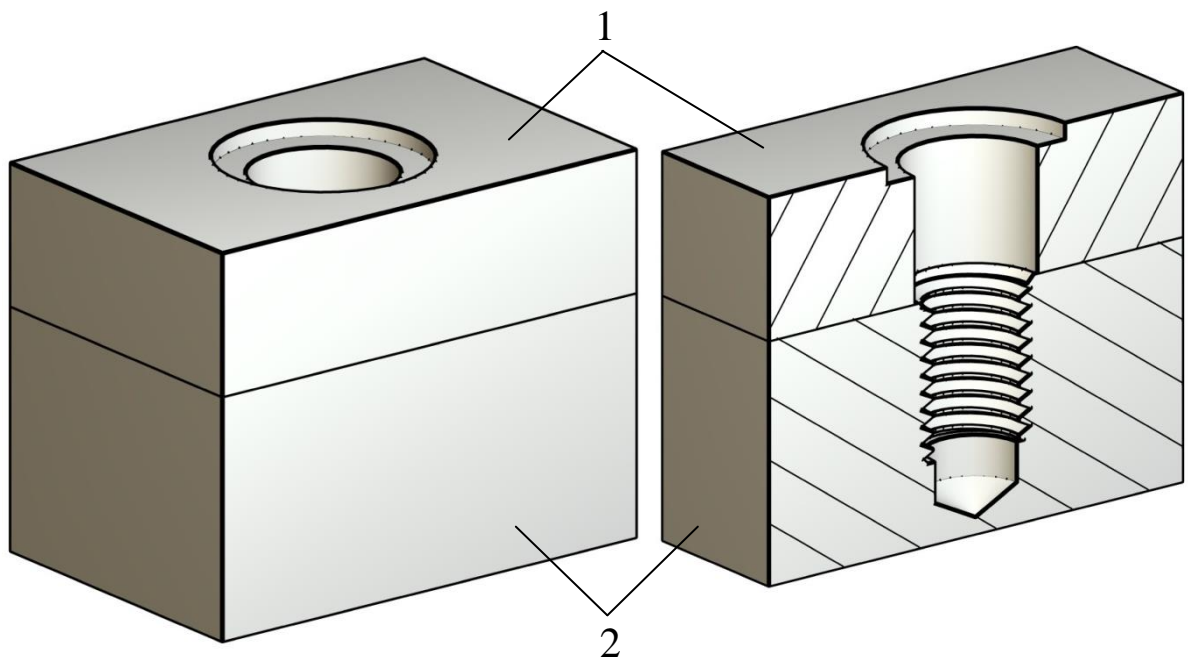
Детали, соединяемые посредством стандартных крепежных изделий (справа изображение выполнено условно в разрезе): 1 – присоединяемая деталь с отверстием под винт и посадочным углублением (цековкой) под шайбу; 2 – деталь с резьбовым отверстием
